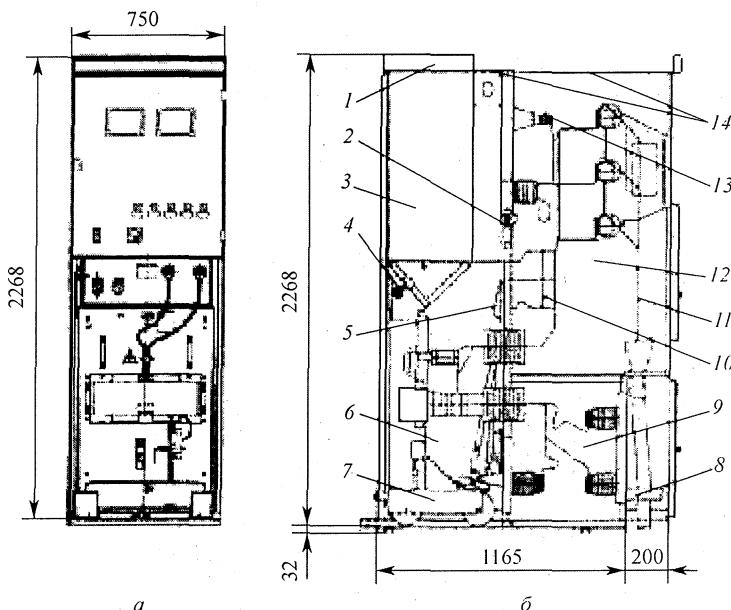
Камера К-63 кабельного ввода (вывода) с подключением в камере: а — вид спереди; б — вид сбоку; 1 — лоток; 2 — заземляющий разъединитель; 3 — релейный шкаф; 4 — блокировочный замок; 5 — шторный механизм; 6 — отсек выкатного элемента; 7 — выкатной элемент с выключателем типа ВВ/TEL; 8 — трансформатор тока ТДЗЛ; 9 — отсек сборных шин; 10 — ТТ; 11 — силовой кабель; 12 — отсек ввода; 13 — ОПН; 14 — клапаны разгрузки избыточного давления
